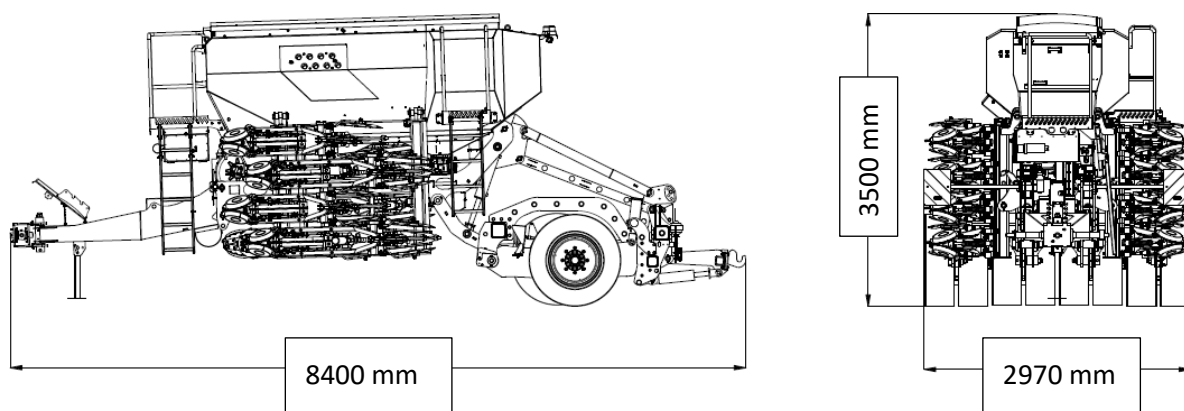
Gesamtabmessungen der 3 m langen Maschine ohne Aufsatz
